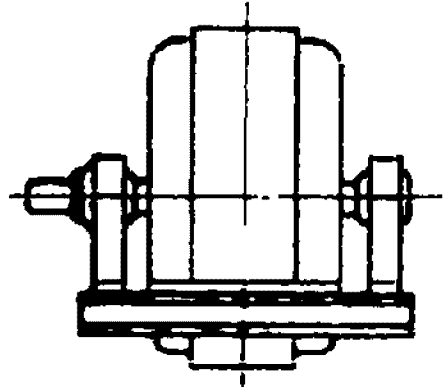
Общий вид машины со стоячковыми подшипниками
